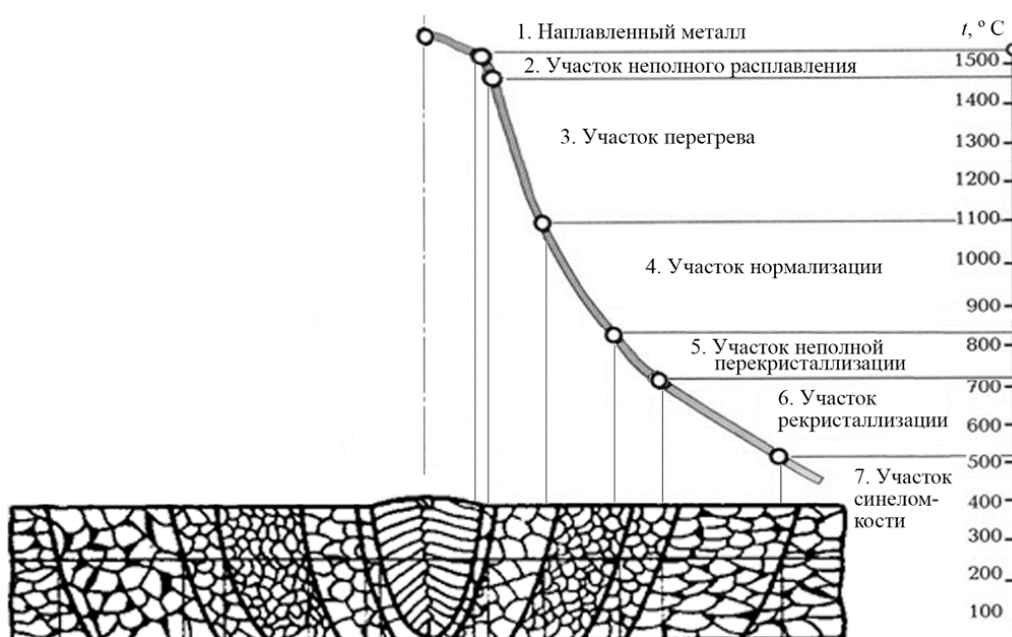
Схема строения сварного соединения при дуговой сварке стали
